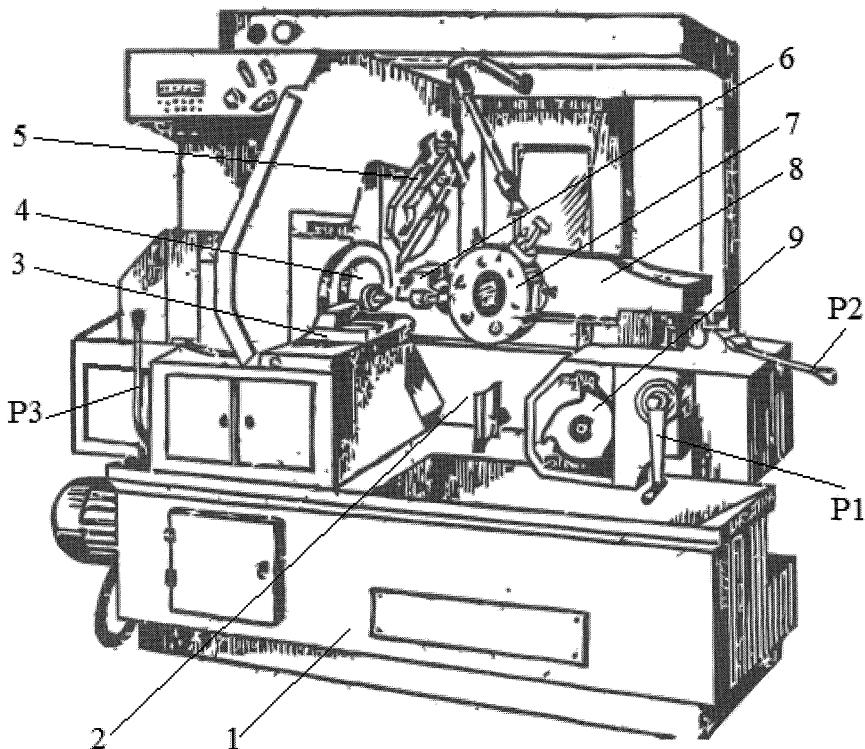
Общий вид токарно-револьверного автомата 1Е125
